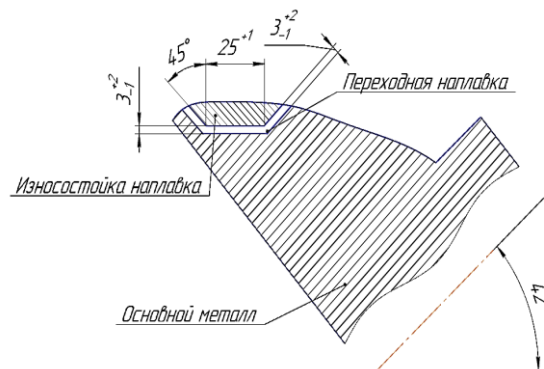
Равномерная толщина наплавки, стабильно высокая твердость и высокое качество
